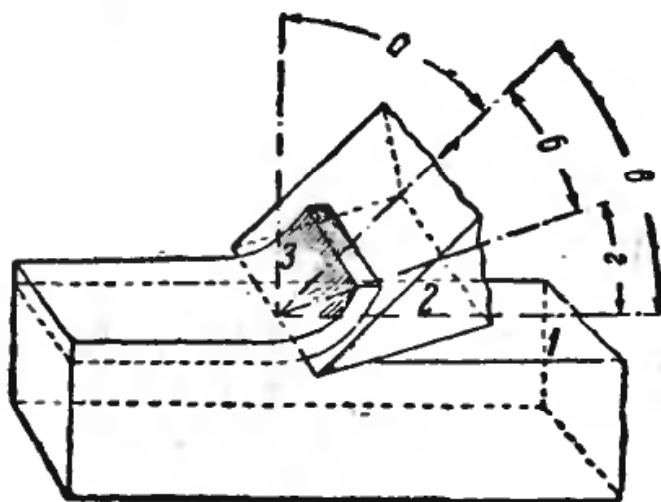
Элементы резца: 1 — обрабатываемая резцом поверхность; часть её, расположенная впереди резца, называется передней, сзади резца — задней; 2 — резец; 3 — снимаемая резцом стружка; б — угол, образуемый передней и задней гранью резца (фаской), называется углом заострения или углом заточки; в — угол, образуемый передней гранью резца и задней частью поверхности резания, называется углом резания; г — угол, образованный задней гранью (фаской) резца и задней частью поверхности резания — задний угол; а — угол, образованный передней гранью резца и перпендикуляром к поверхности обрабатываемой детали из любой точки лезвия, — передний угол.
